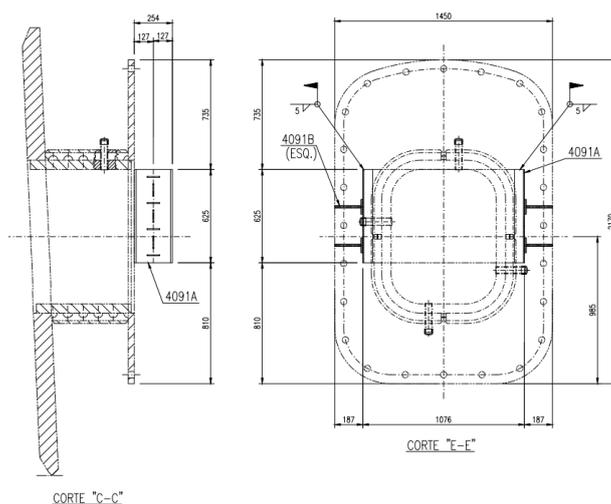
Ilustração da projeção soldada na parte frontal da capela
